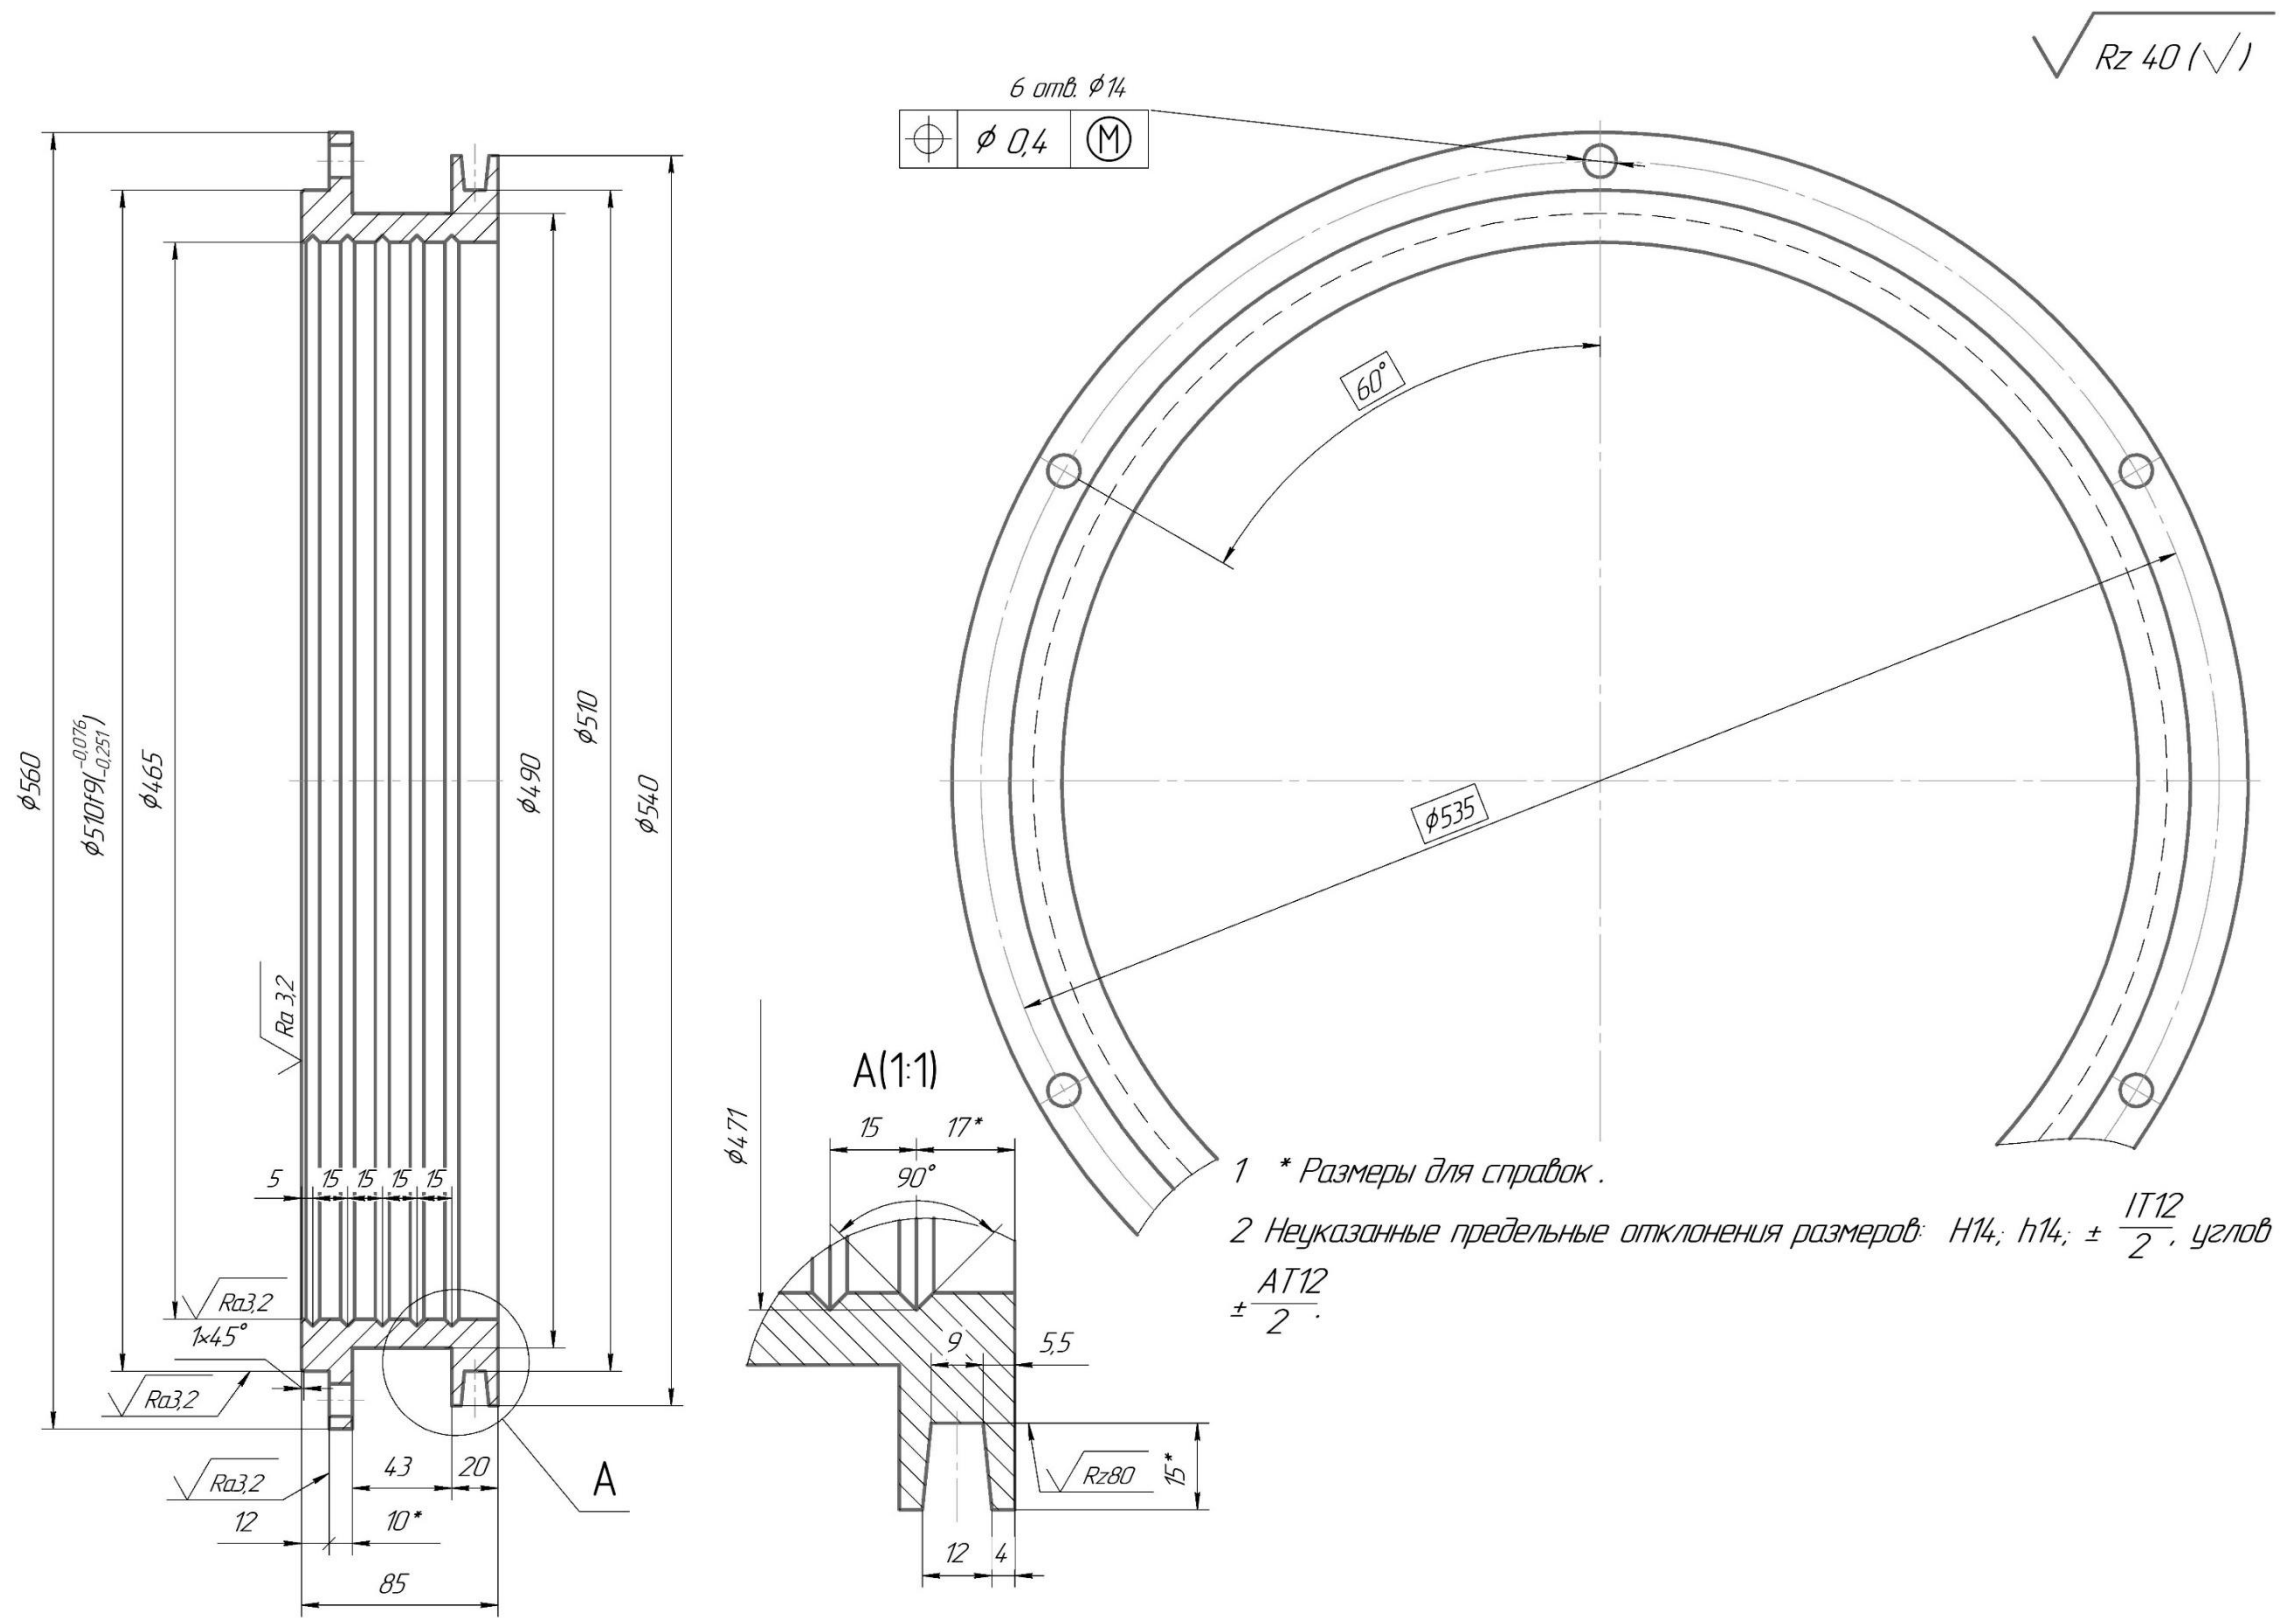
Чертеж кольца ТПА 220 из стали 45 ГОСТ 1050–2013 [62]
